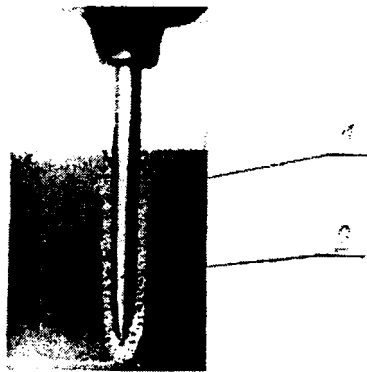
Обработка заготовки в рабочей зоне: 1 – ферропорошок; 2 – заготовка
